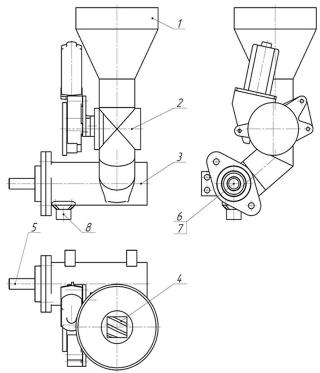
Конструкция разрабатываемого высевающего аппарата: 1 — бункер для семян; 2 — корпус дозатора; 3 — корпус шнека высевающего аппарата; 4 — катушка дозатора; 5 — приводной вал катушки дозатора; 6 — шнек высевающего аппарата; 7 — приводной вал шнека высевающего аппарата; 8 — выходное окно
